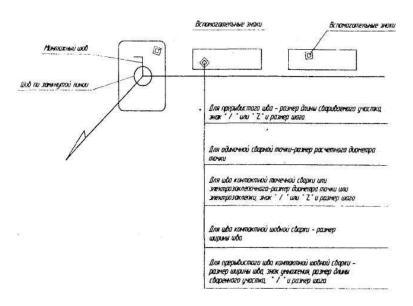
Структура условного обозначения нестандартного шва или одиночной сварной точки
